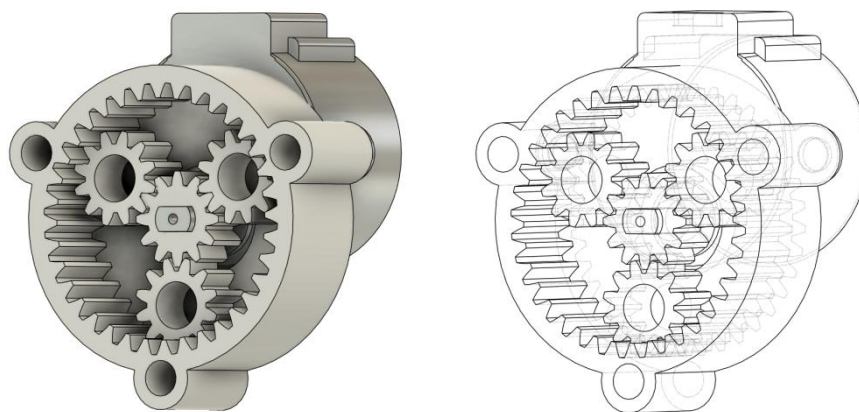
Планетарний редуктор 4:1 у розрізі
